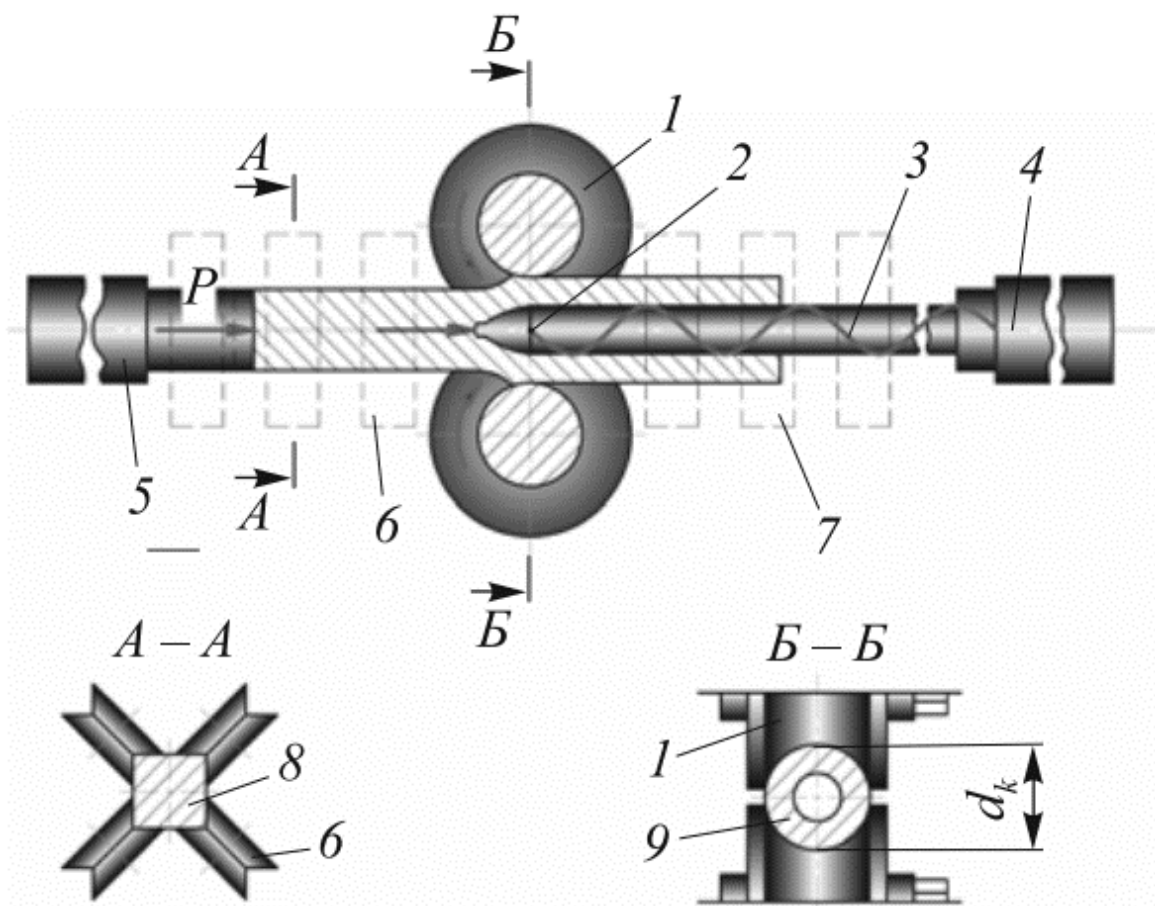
Схема пресс-валковой прошивки: 1 – валковая клеть; 2 – оправка; 3 – стержень; 4 – упорно-регулирующий механизм; 5 – вталкиватель заготовки; 6 – роликовые проводки; 7 – центрователь стержня оправки и гильзы; 8 – заготовка; 9 – гильза (труба)
